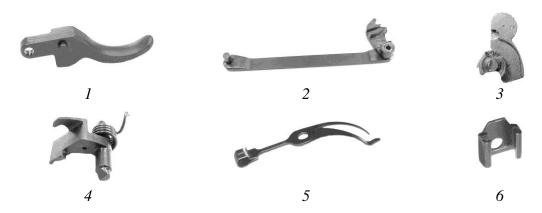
Ударно-спусковой механизм: 1 — спусковой крючок; 2 — спусковая тяга с рычагом взвода; 3 — курок; 4 — шептало с пружиной; 5 — боевая пружина; 6 — задвижка боевой пружины
